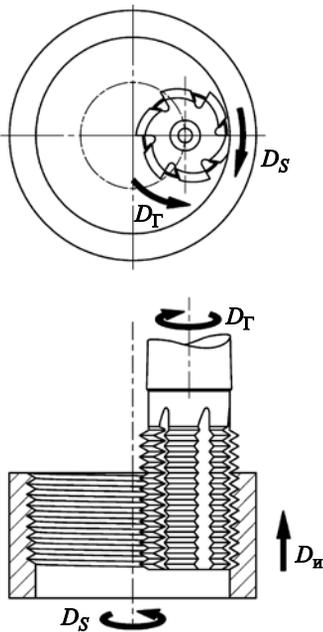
Фрезерование внутренней резьбы гребенчатой концевой фрезой
